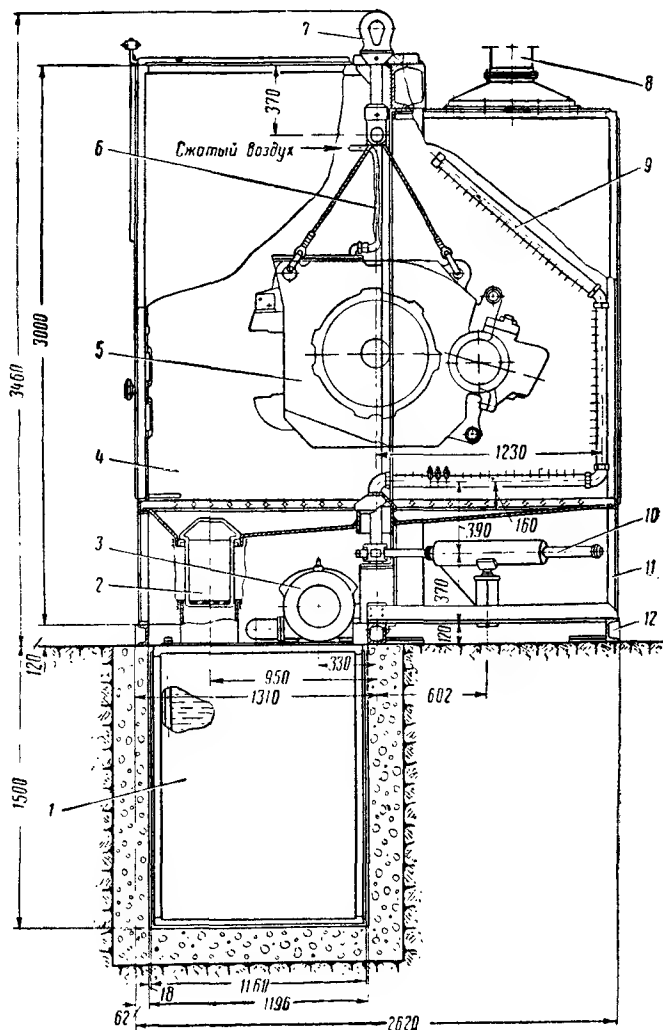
Моечная установка для предварительной очистки тяговых двигателей перед разборкой:
